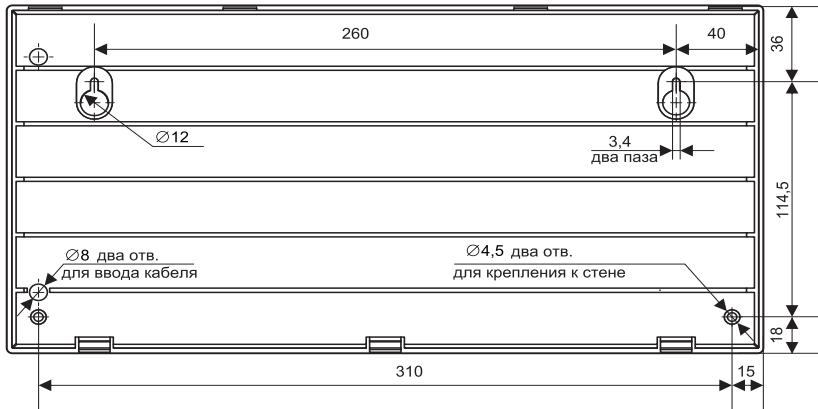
Внешний вид, габаритные и установочные размеры блока «С2000-ПТ»
